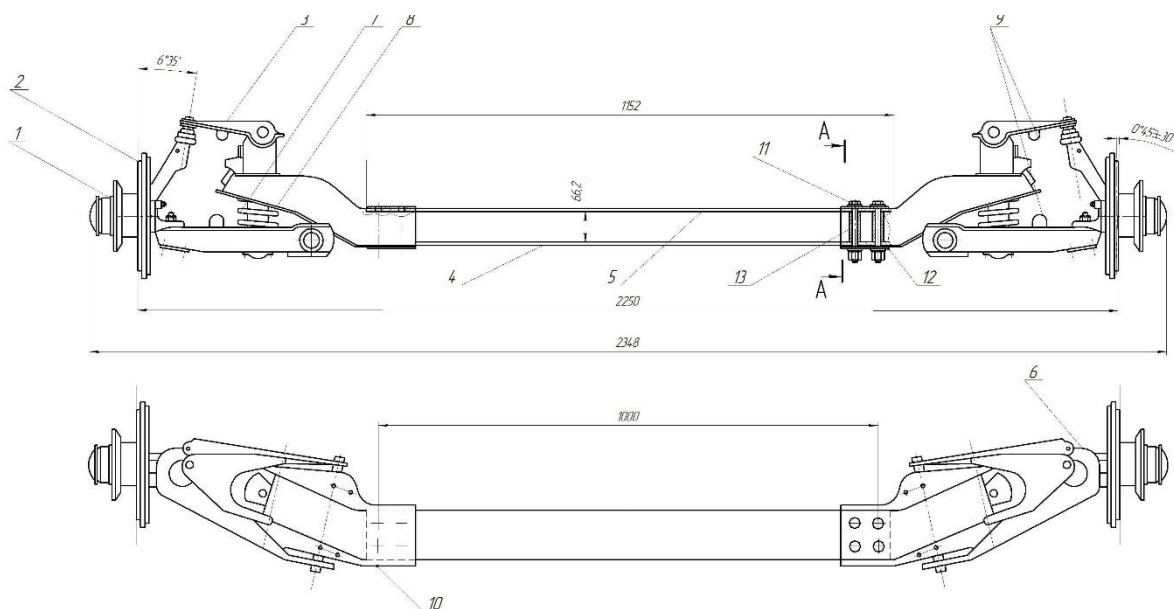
Подвеска передняя: 1- ступица; 2- тормозной диск; 3- верхний рычаг; 4- нижняя проставка; 5- верхняя проставка; 6- нижний рычаг; 7- пружина; 8- амортизатор; 9- буфер; 10- балка; 11- стяжной болт; 12- проставка усилительная; 13- втулка распорная
